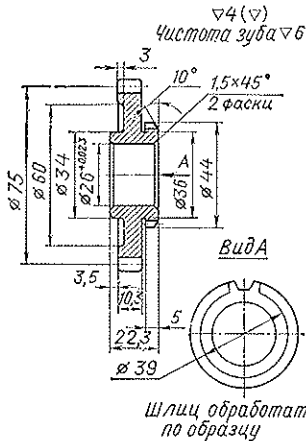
Вторичный вал. Шестерня четвертой передачи. Данные для изготовления; число зубьев — 30; n — 58,6; m — 2,5; α — 20°; D_{e2} — 81,1; h — 5,625; d — d_2 — 75.
